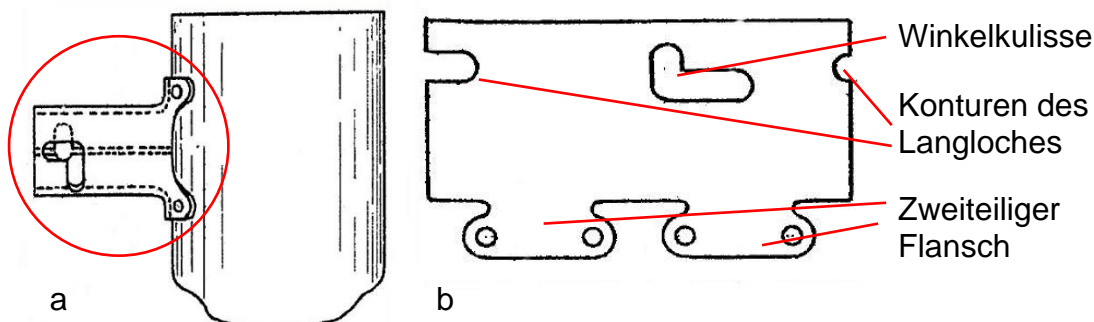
Kombination aus Drehbolzen und zweiteiligem Flansch: a) Rohrförmiger Drehbolzen am Gehäusemantel angenietet, b) Blechschnitt
